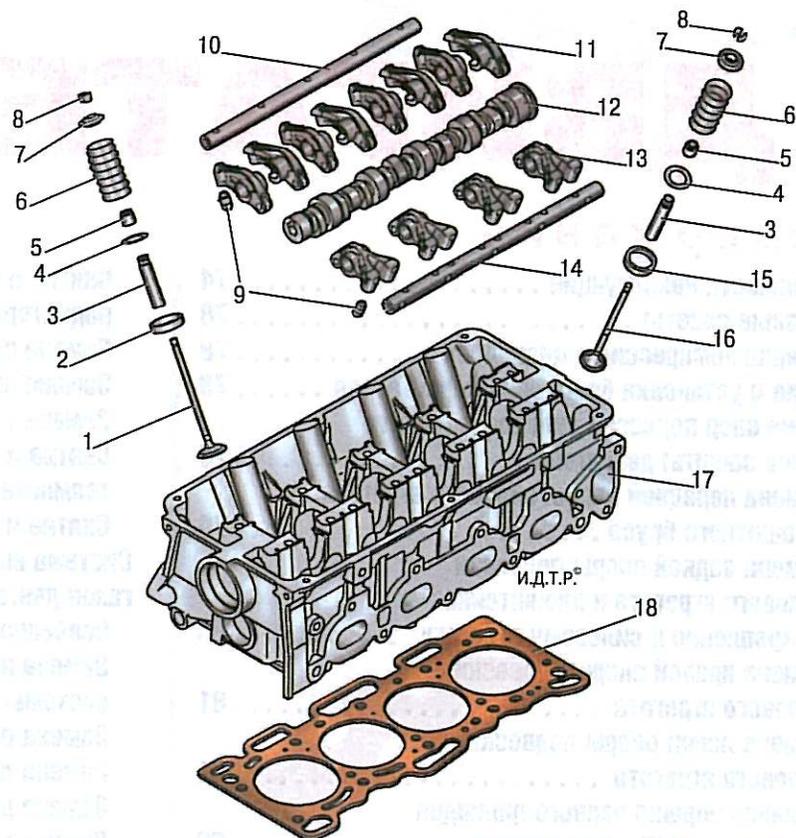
Головка блока цилиндров двигателя SOHC: 1 – впускной клапан; 2 – седло впускного клапана; 3 – направляющая втулка клапана; 4 – опорная шайба пружины клапана; 5 – маслосъемный колпачок; 6 – пружина клапана; 7 – тарелка пружины клапана; 8 – сухарь; 9 – гидрокompенсатор зазоров в механизме привода клапанов; 10 – ось коромысел впускных клапанов; 11 – коромысло впускного клапана; 12 – распределительный вал; 13 – коромысло выпускного клапана; 14 – ось коромысел выпускных клапанов; 15 – седло выпускного клапана; 16 – выпускной клапан; 17 – головка блока цилиндров; 18 – прокладка головки блока цилиндров
